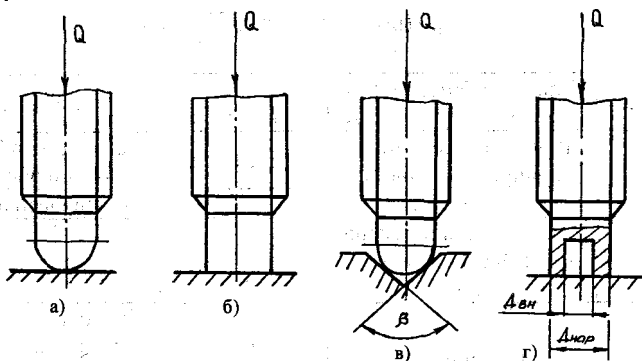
Виды опорных поверхностей зажимных механизмов приспособлений
